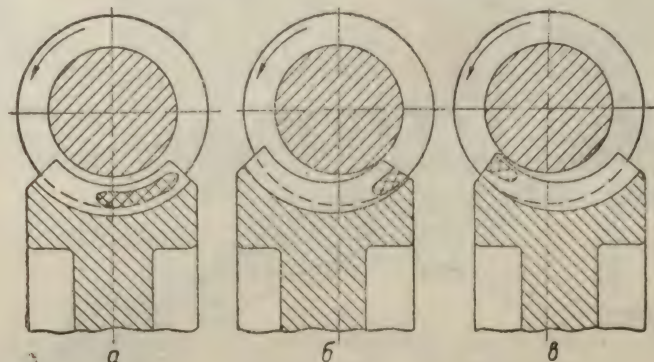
Проверка зацепления по отпечатку краски в зубьях червячного колеса:
